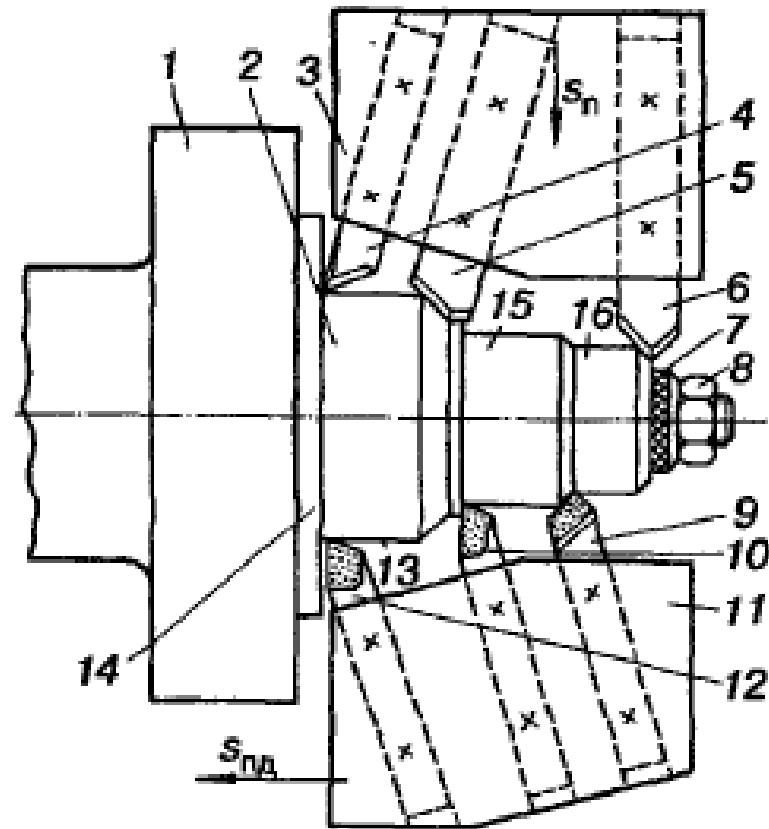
Схема обробки на багато різцевому токарному верстаті
